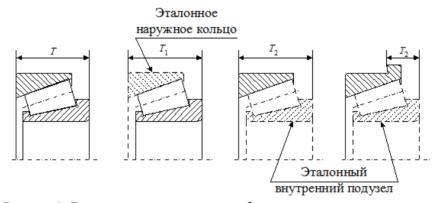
Дополнительные условные обозначения основных размеров роликовых конических подшипников
